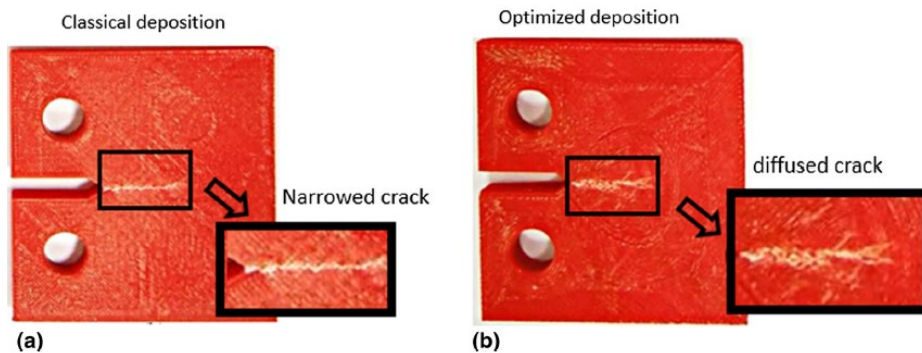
12 Propagación de grietas en el trabajo de Gardan et al. [41]
